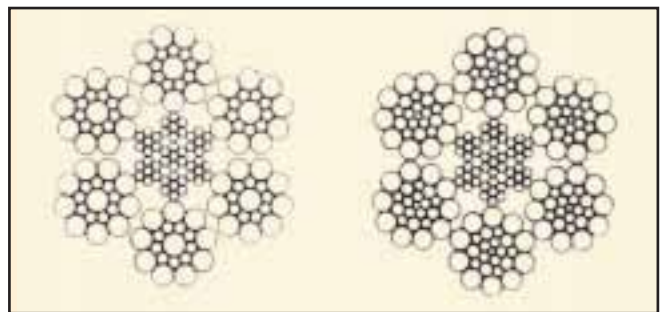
Configuración y disposición de los elementos del cable de perforación.
